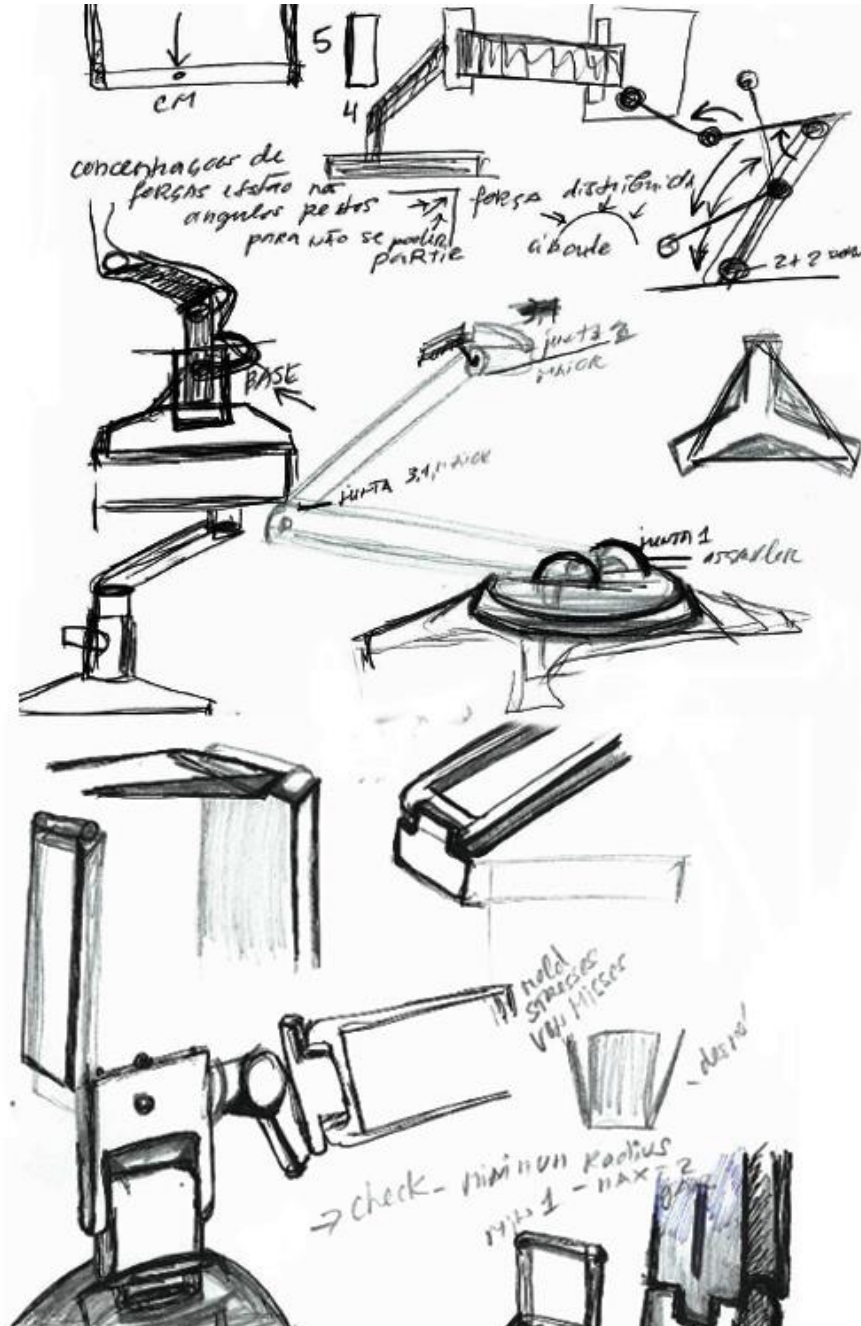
Esboços iniciais e estudo de construção das peças para o candeeiro
